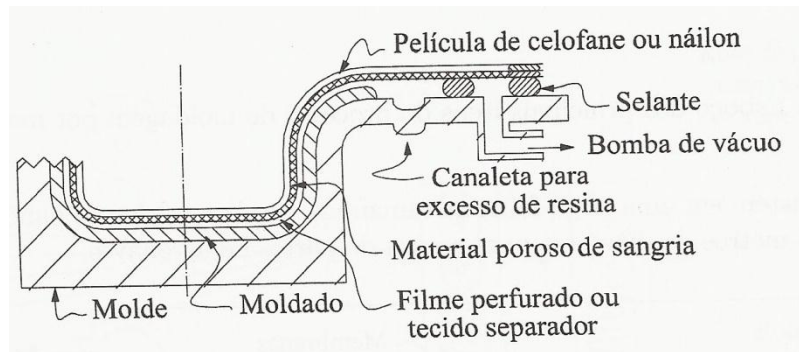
Moldagem à vácuo - (MENDONÇA, 2005)
